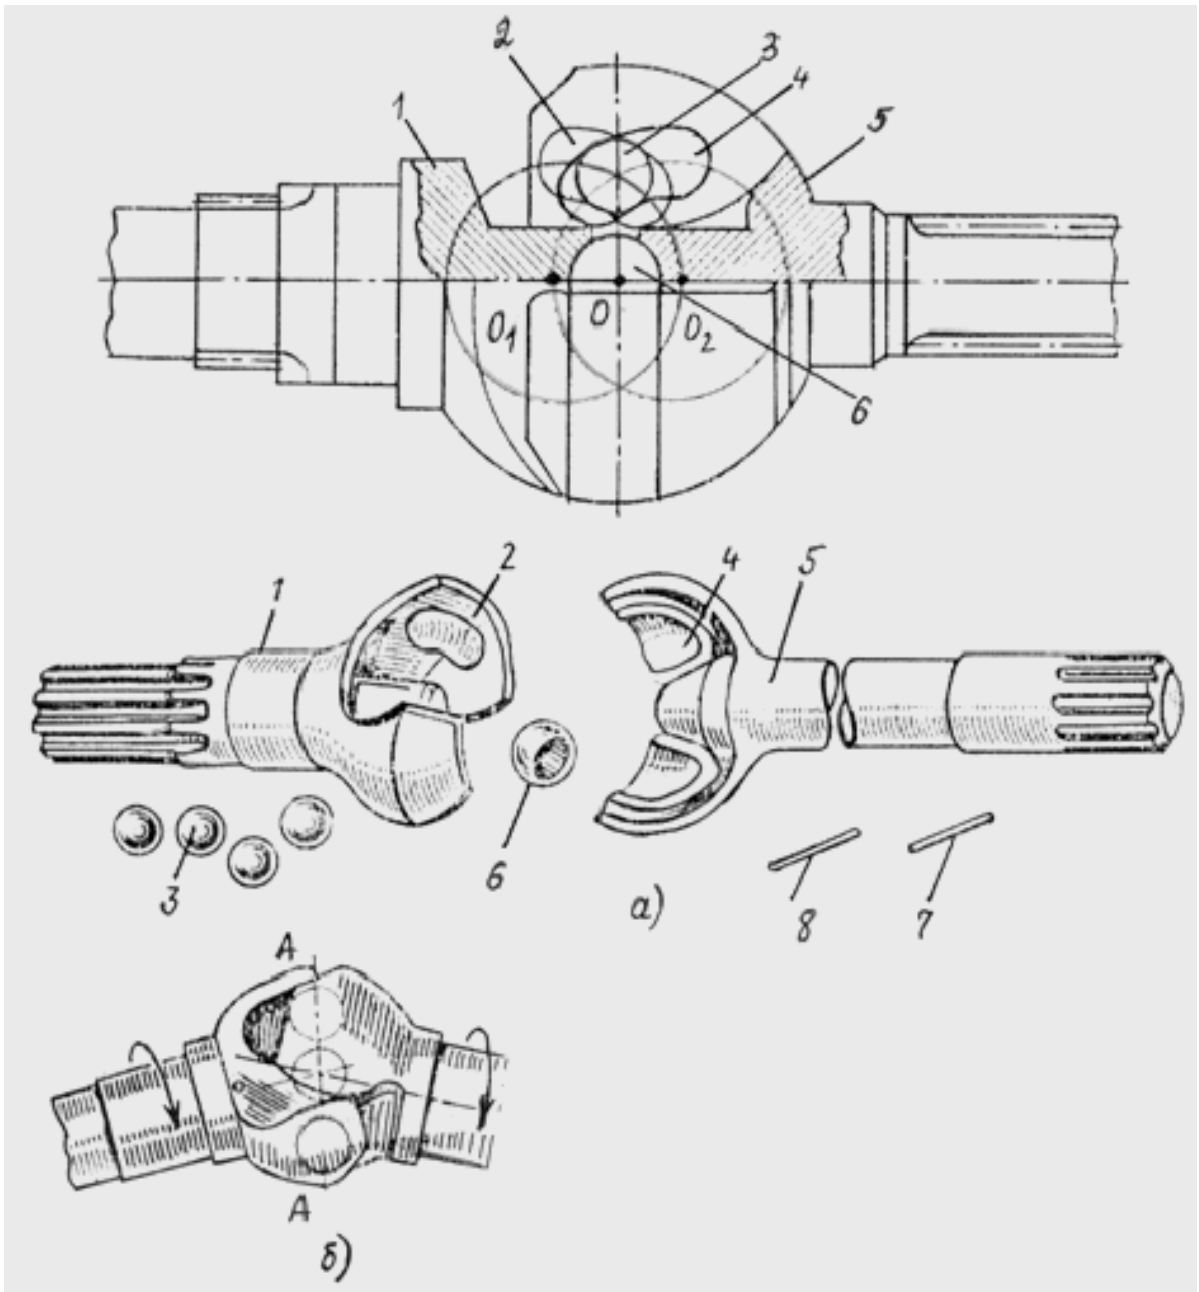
Шариковый карданный шарнир равных угловых скоростей с делительными канавками: а – продольный разрез и детали; б – принцип действия; 1, 5 - вилки; 2, 4 - криволинейные канавки; 3, 6 - шарики; 7, 8 - шпильки; 9 - установочное кольцо
